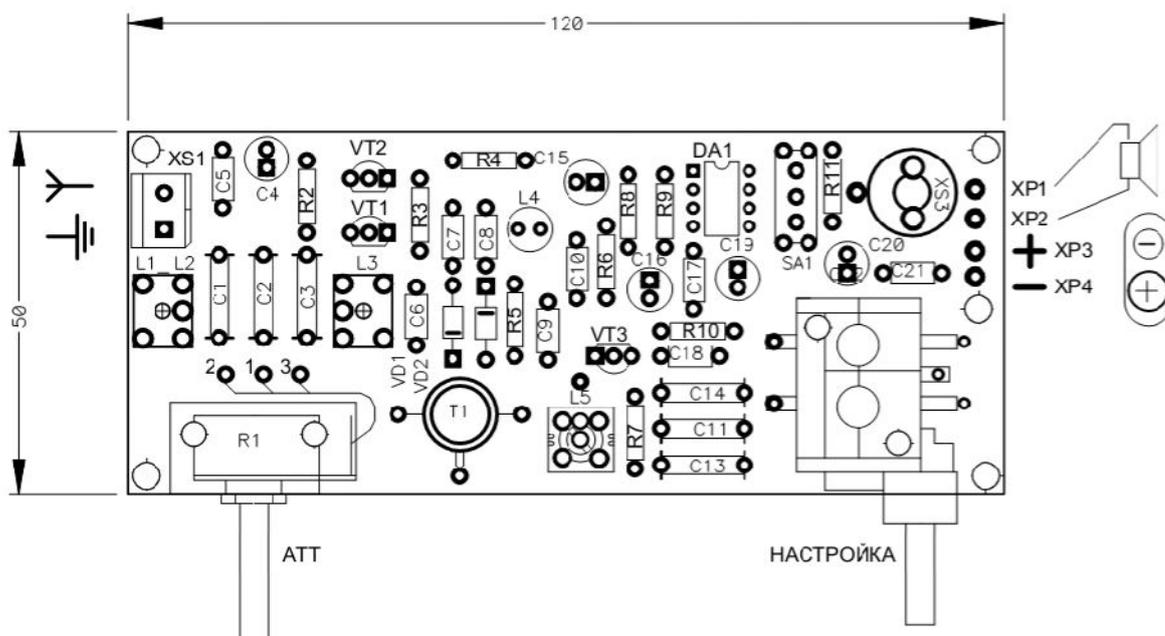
Расположение деталей на плате приемника (сборочный чертеж).
